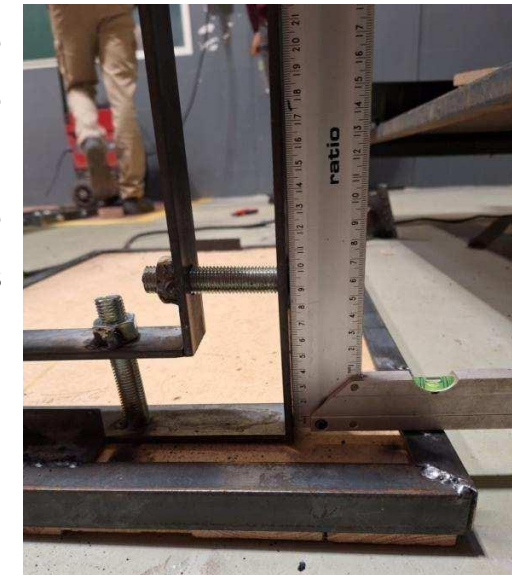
Comprobando que todo quedase a escuadra antes de soldar.
